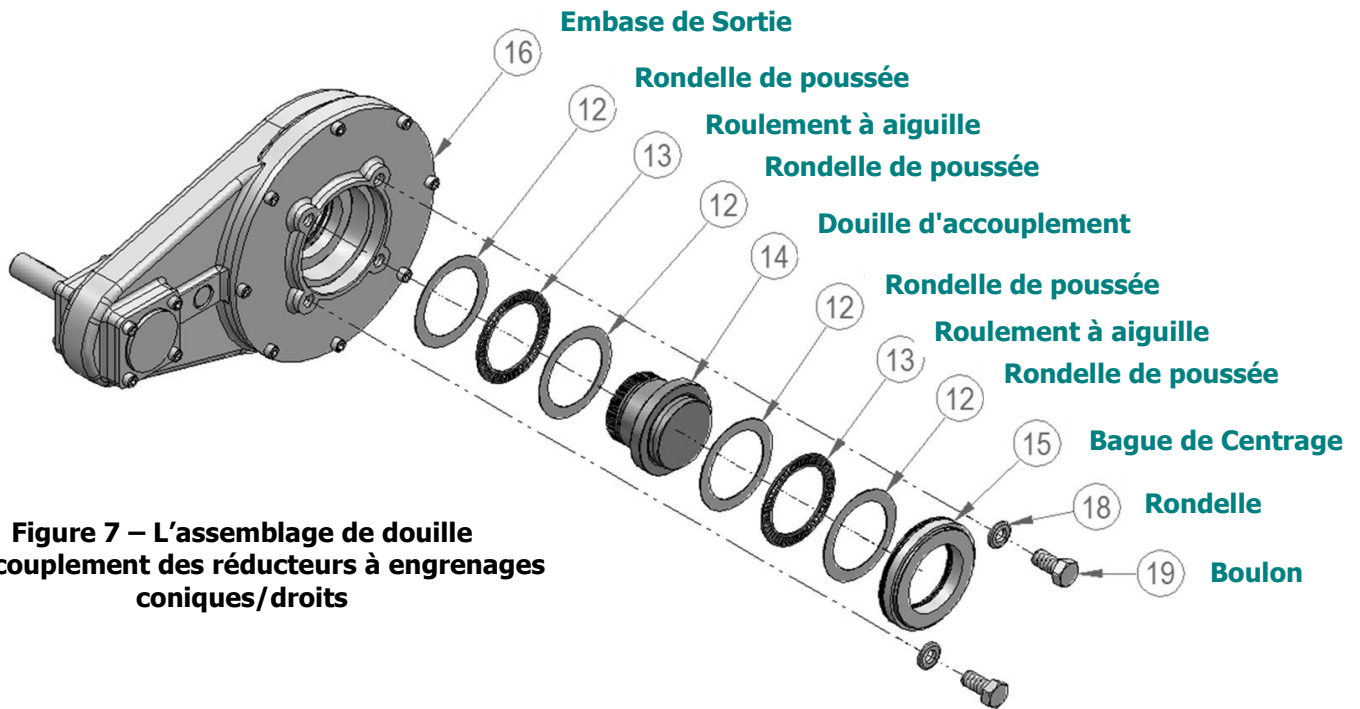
L'assemblage de douille d'accouplement des réducteurs à engrenages coniques/droits
